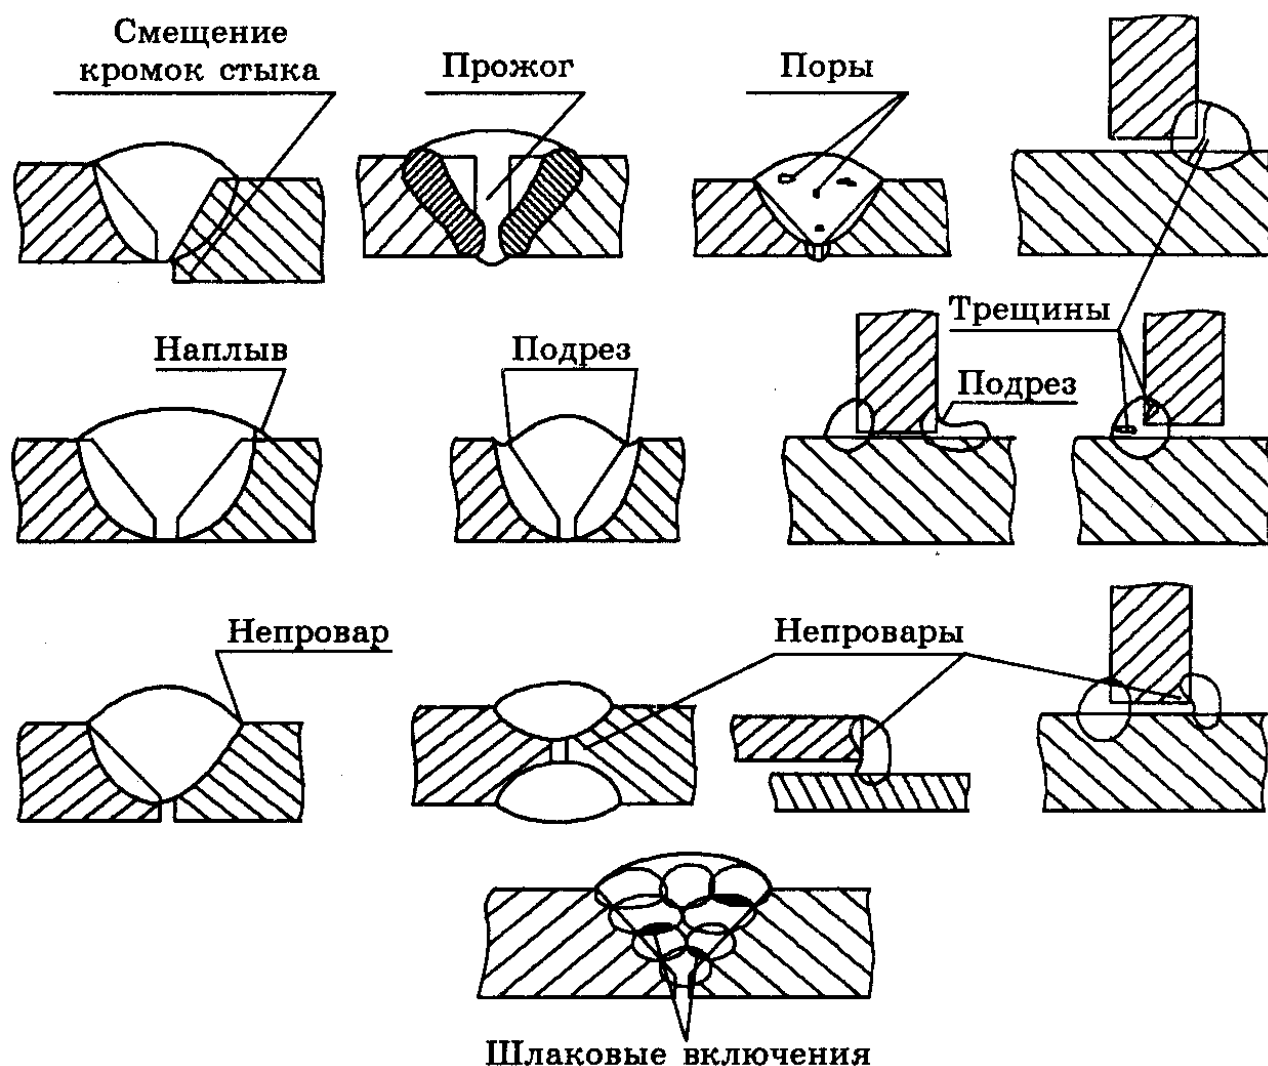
Макроскопические дефекты сварных соединений
